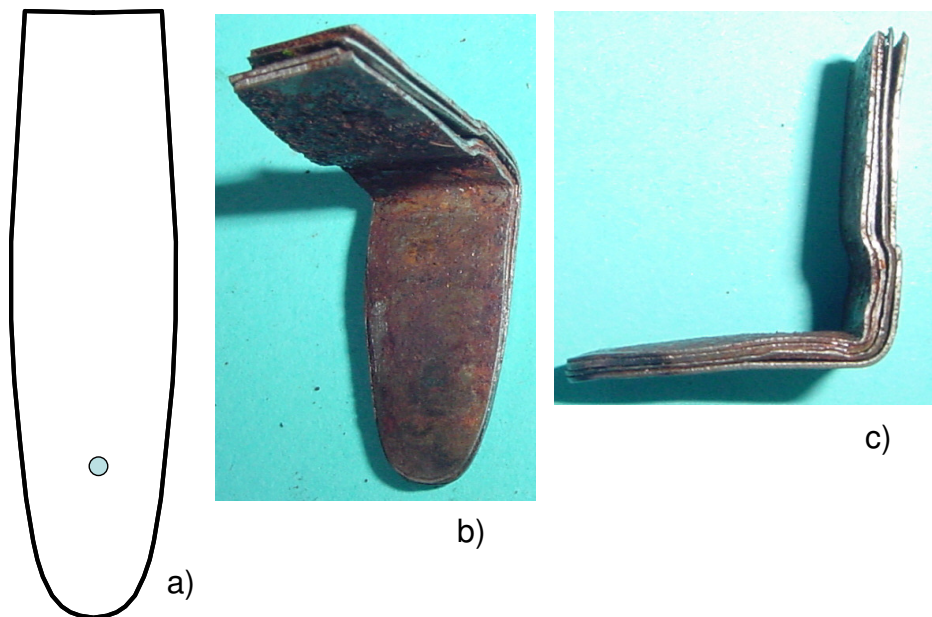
Klauenpolschuh: a) Blechschnitt mit Schweißpunkt, b) und c) senkrecht abgewinkeltes Blechpaket
